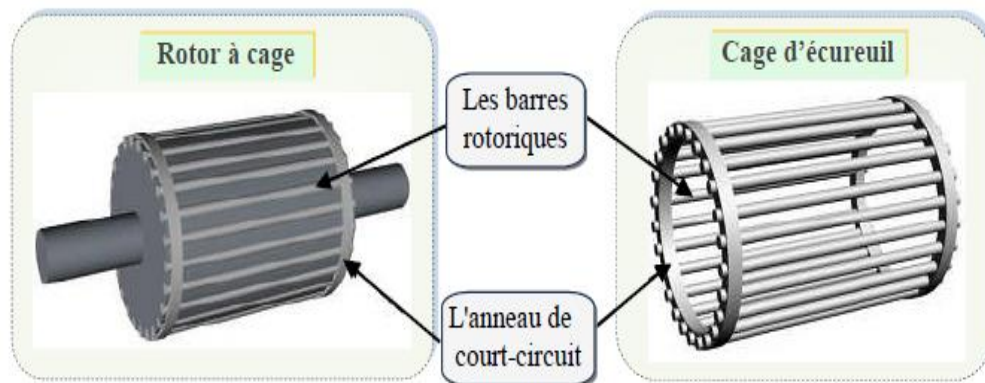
rotor de la machine asynchrone triphasée a cage [6].
